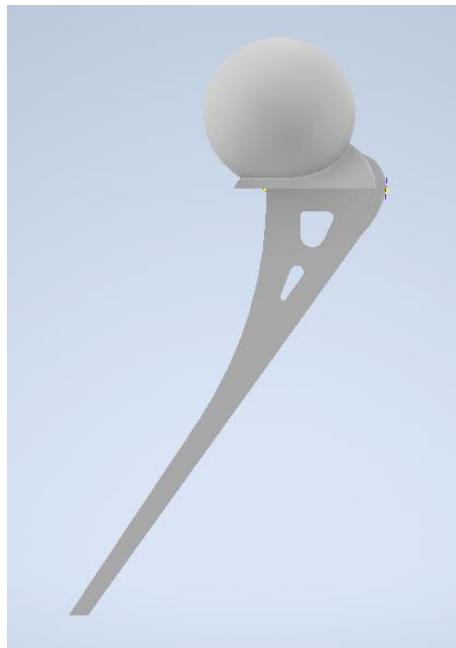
CAD con medidas de tolerancia.
